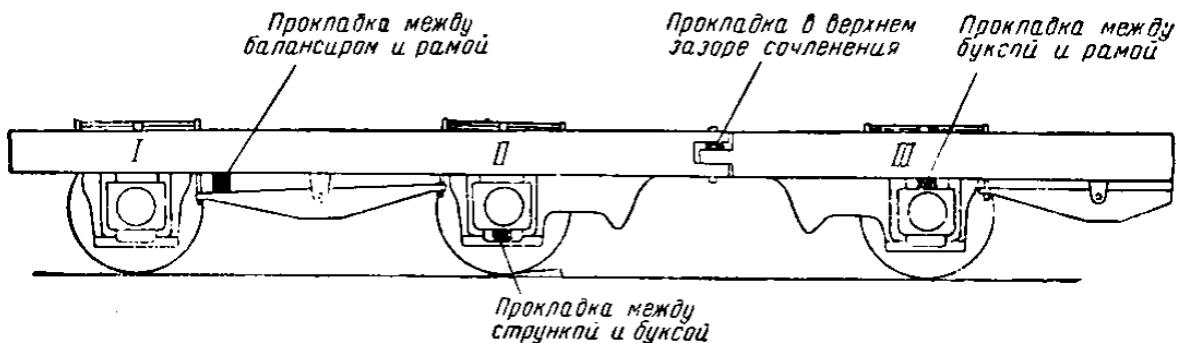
Расположение приспособлений при вывешивании второй колесной пары
